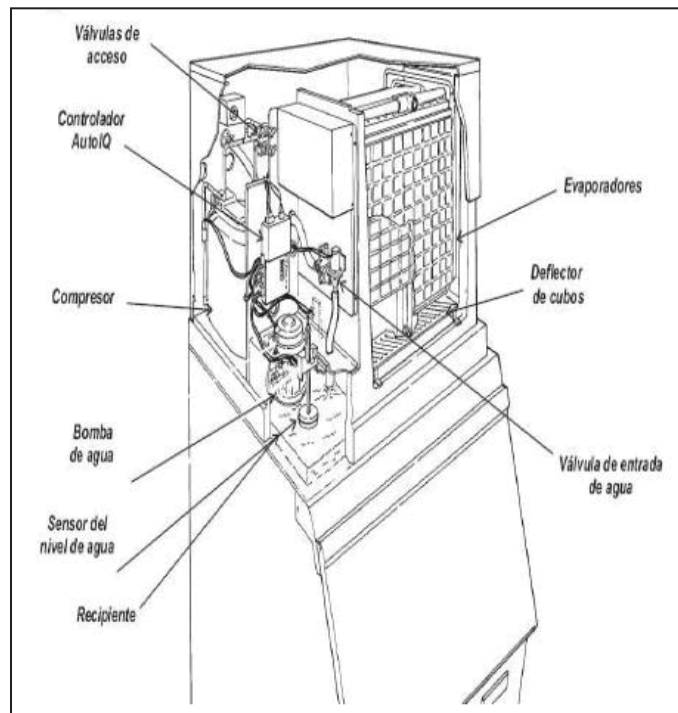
Máquina industrial generadora de cubos de hielos, indicando cada una de las partes que lo integran.
